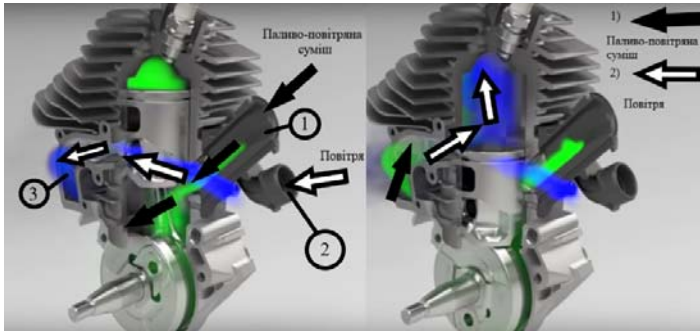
Схема продувки двигуна Husqvarna X-Tool
